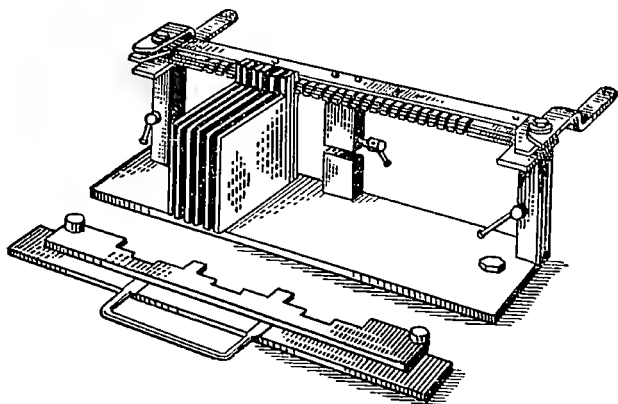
Шаблон для сборки аккумуляторных пластин в полублоки.
